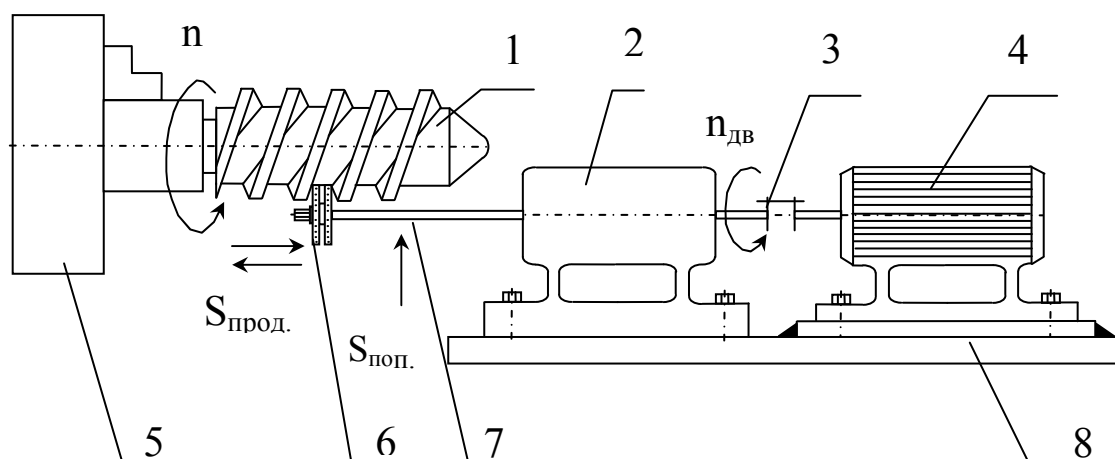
Схема обработки наружной винтовой поверхности червяка: 1 - обрабатываемая деталь – червяк; 2 – люнет; 3 – муфта; 4 – двигатель; 5 – патрон; 6 - набор полимер-абразивных кругов; 7 – оправка; 8 - плита.
